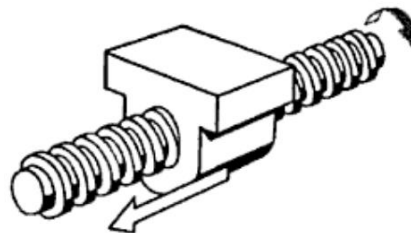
Husillo de Roscar. Fuente: W. Bartsch, 1966
